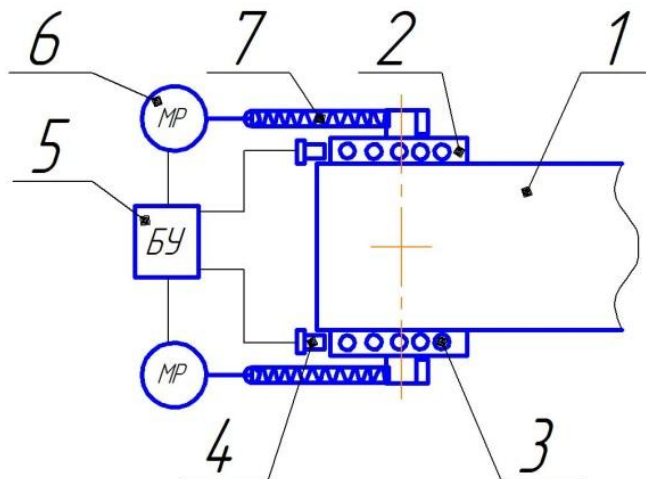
Схема установки для автоматичного натягу стрічки та центрування її положення в горизонтальній площині.
